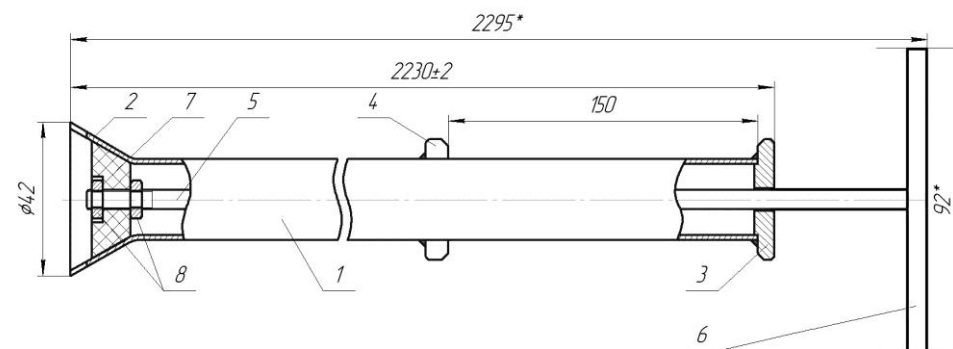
Пробоотборник ППРМ-Т: 1 – корпус; 2 – конус; 3 – направляющая втулка; 4 – упор; 5 – шток; 6 – ручка; 7 – пробка; 8 – гайки.
